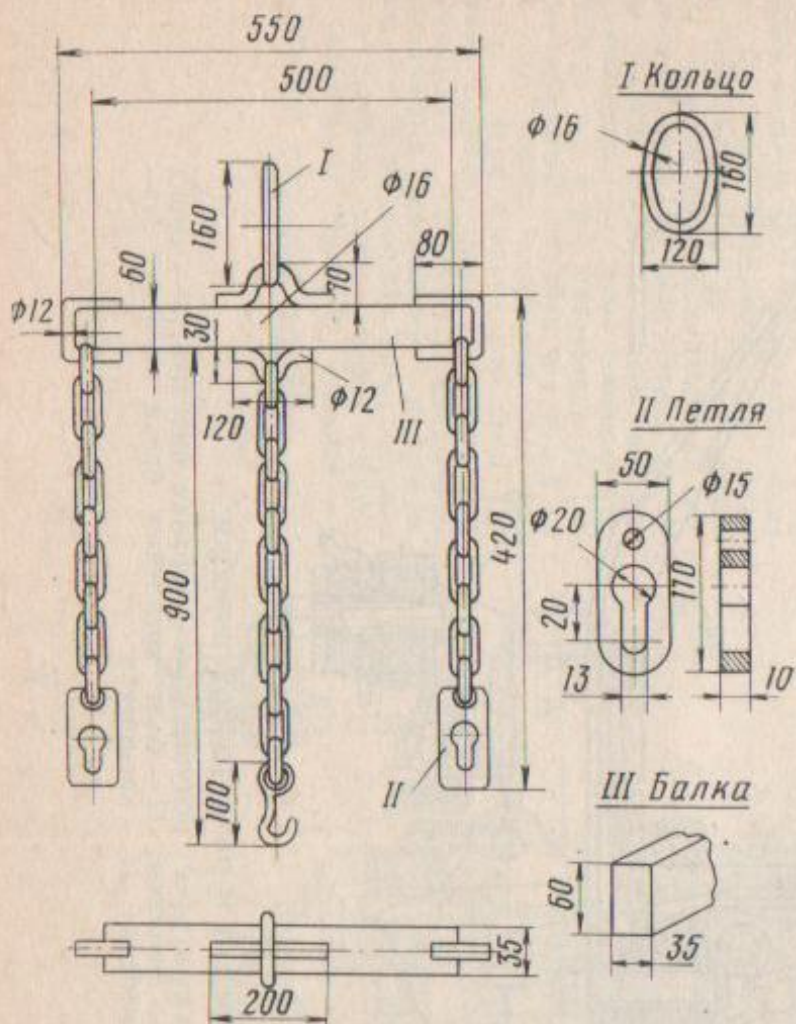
Приспособление для снятия коробки передач с автомобиля
